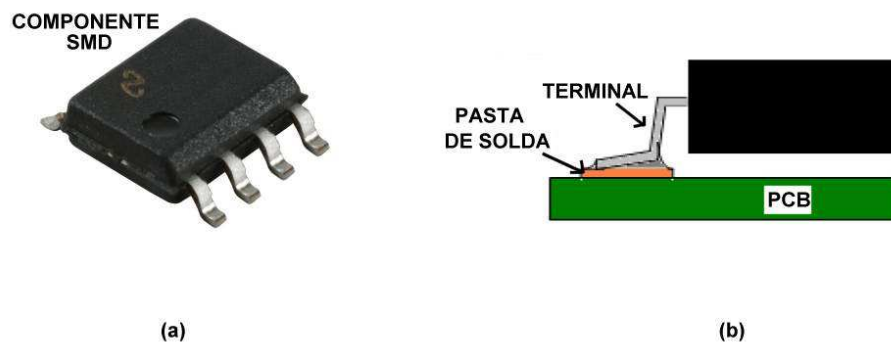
TECNOLOGIA DE MONTAGEM EM SUPERFÍCIE.
